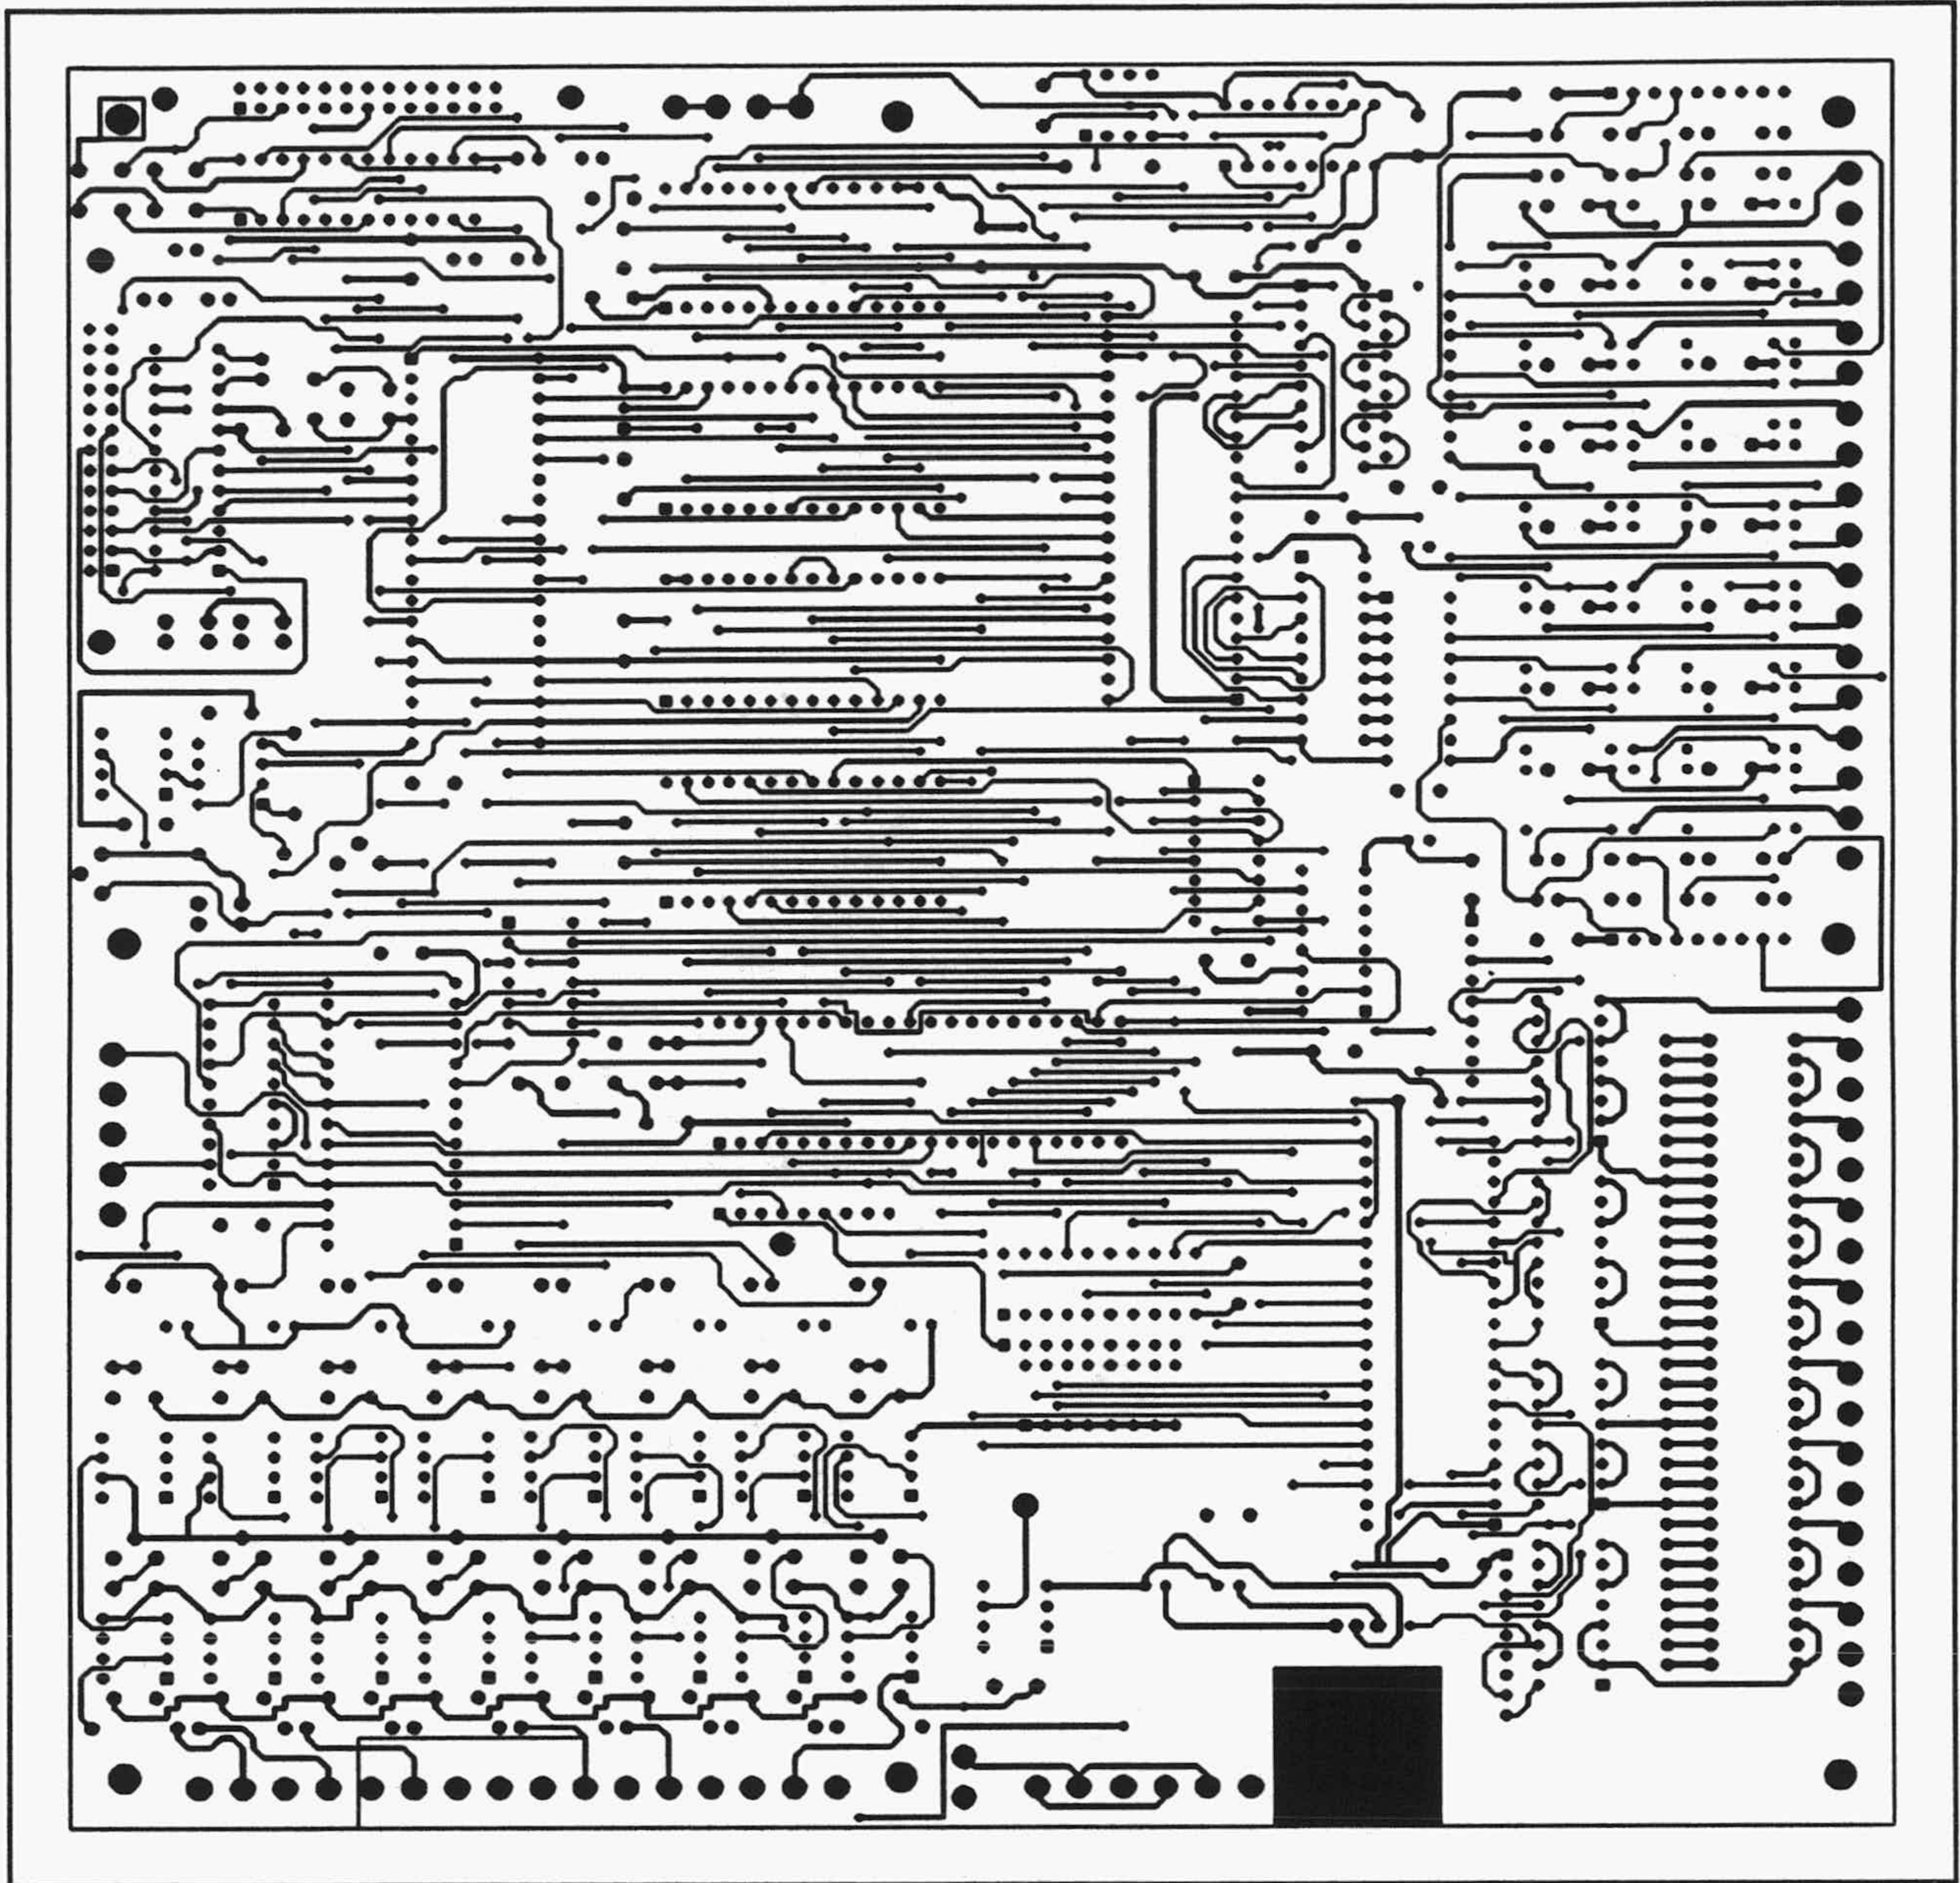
Trazado de pistas de la cara de soldaduras.
